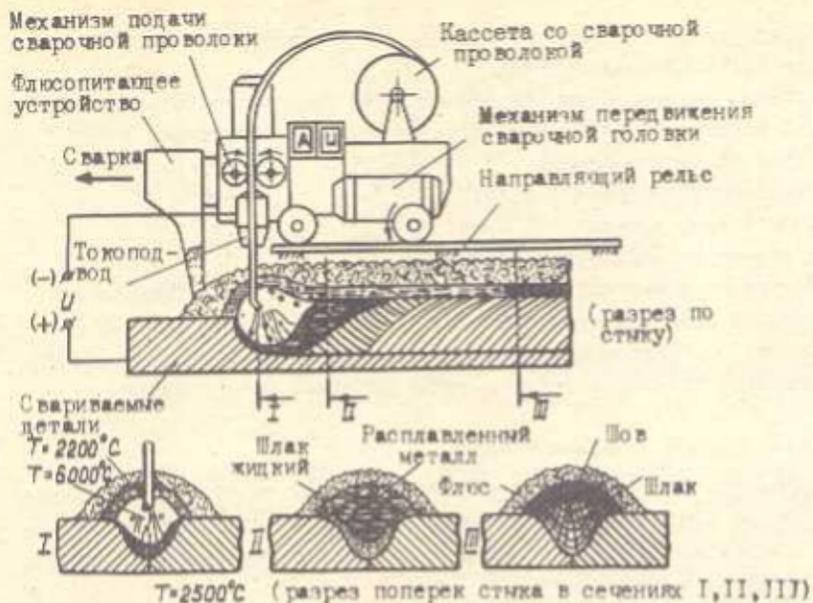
Рис. II. Схема процесса автоматической сварки под флюсом
